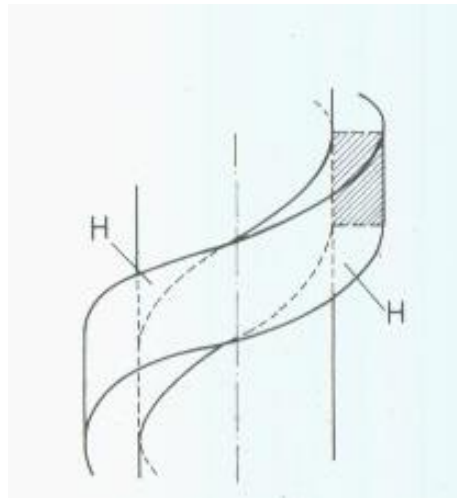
a. Rosca con perfil rectangular (vista en planta)
